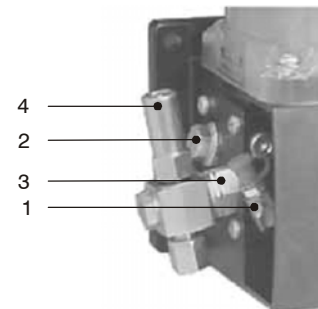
Anschluss Pumpenelemente und Druckbegrenzungsventil
